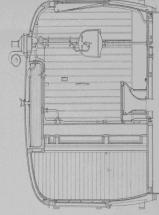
Coupe longitudinale de la caisse pac A B de la fig. 2
